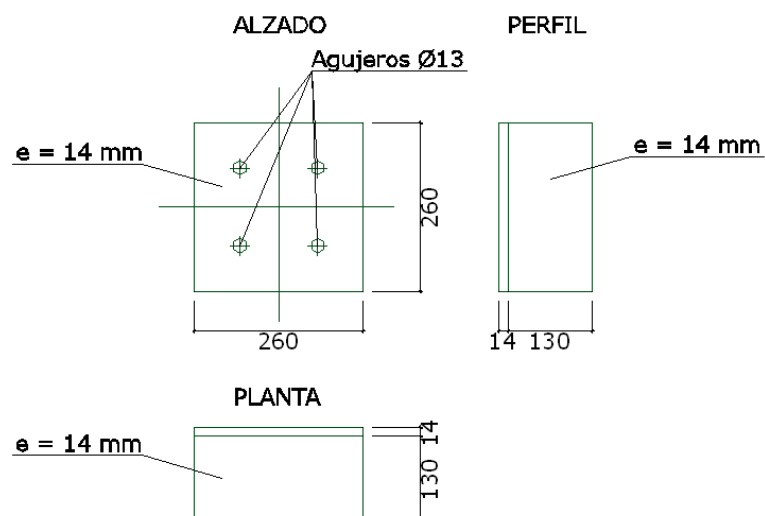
Alzado, planta y perfil del cajón metálico situado en el extremo de la probeta (cotas en mm)
